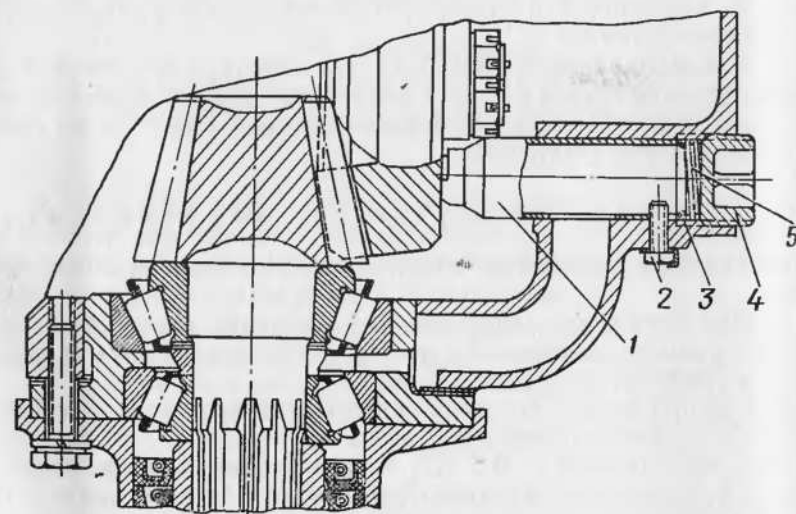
Установка маслоотражателя ведомой шестерни главной передачи:
